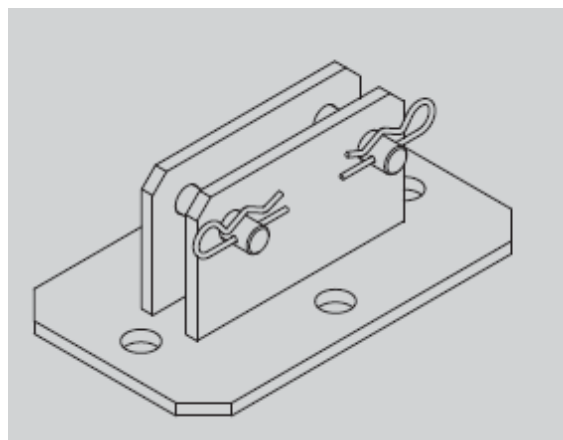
Base estabilizadora. Recuperado de: Ulma Construction, *Catálogo encofrado modular ORMA 60*.
